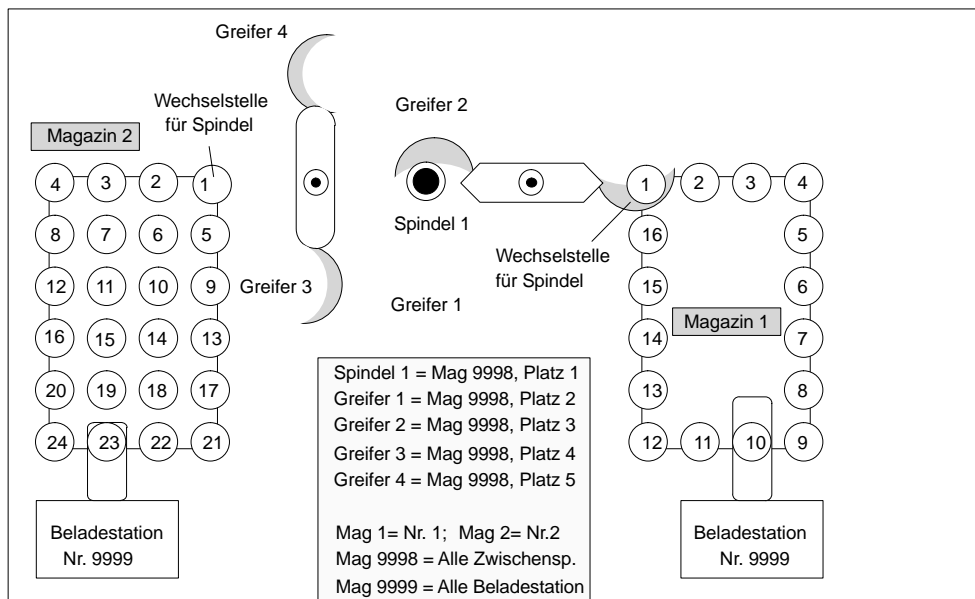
Werkzeugmaschine mit Ketten- und Flächenmagazin
